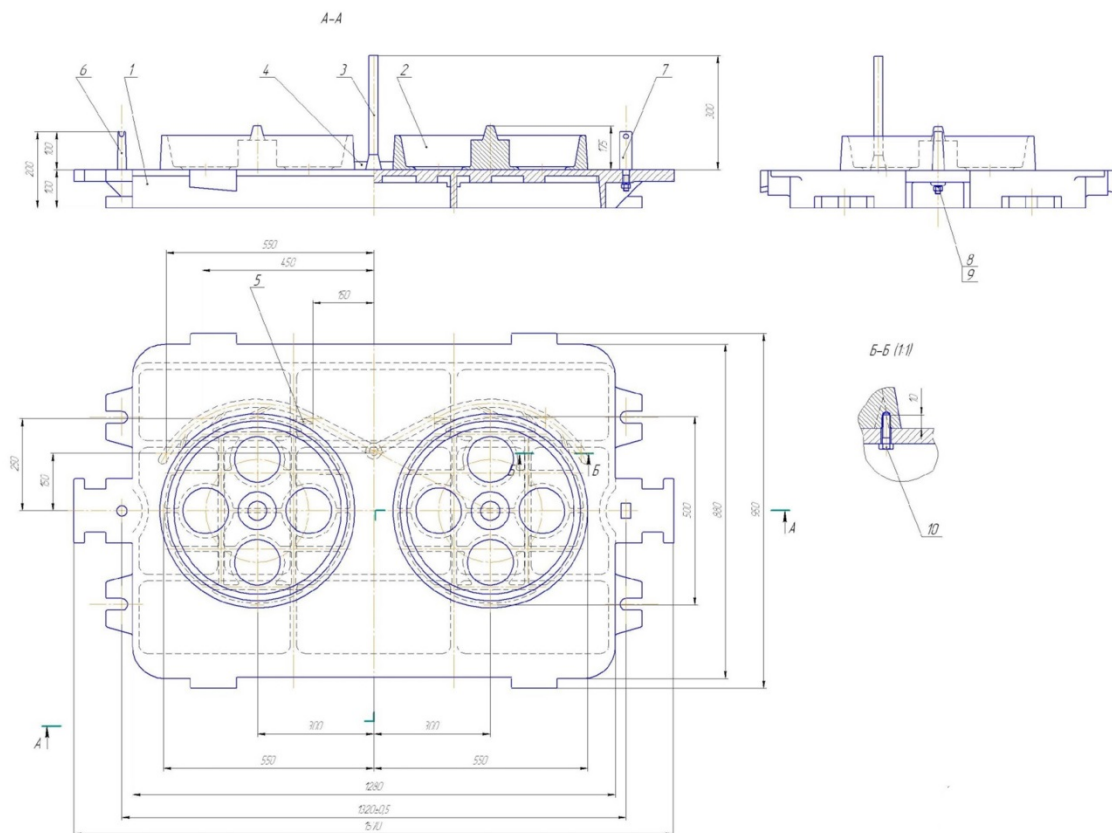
Модельний комплект верху для виготовлення напівформи
